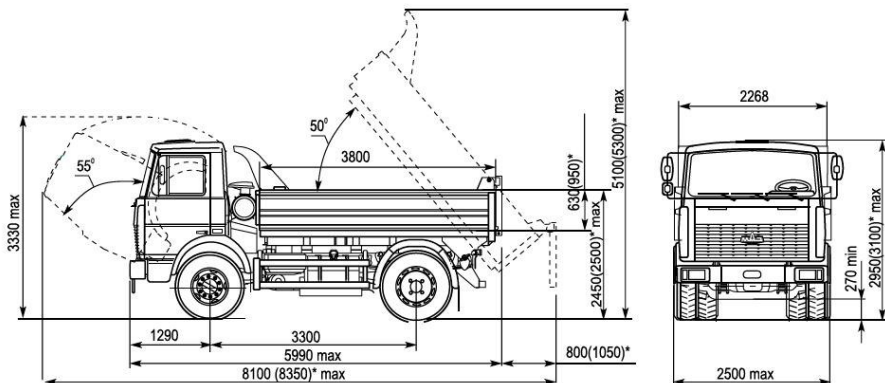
Основные размеры грузового автомобиля МАЗ-5551
